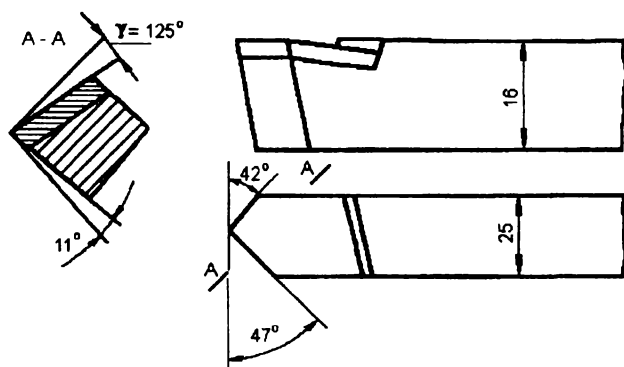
Геометрия резца для проведения испытаний на обрабатываемость
